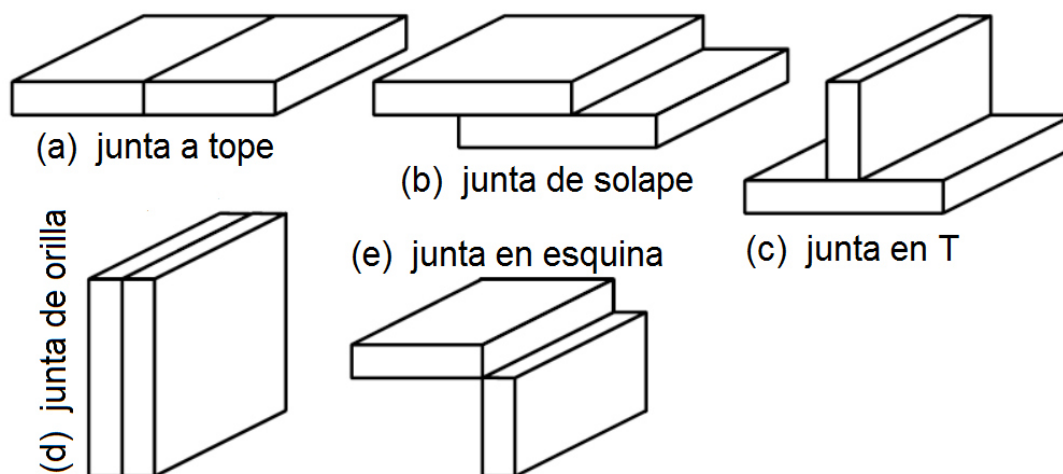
Cinco diseños básicos de juntas de soldadura.
